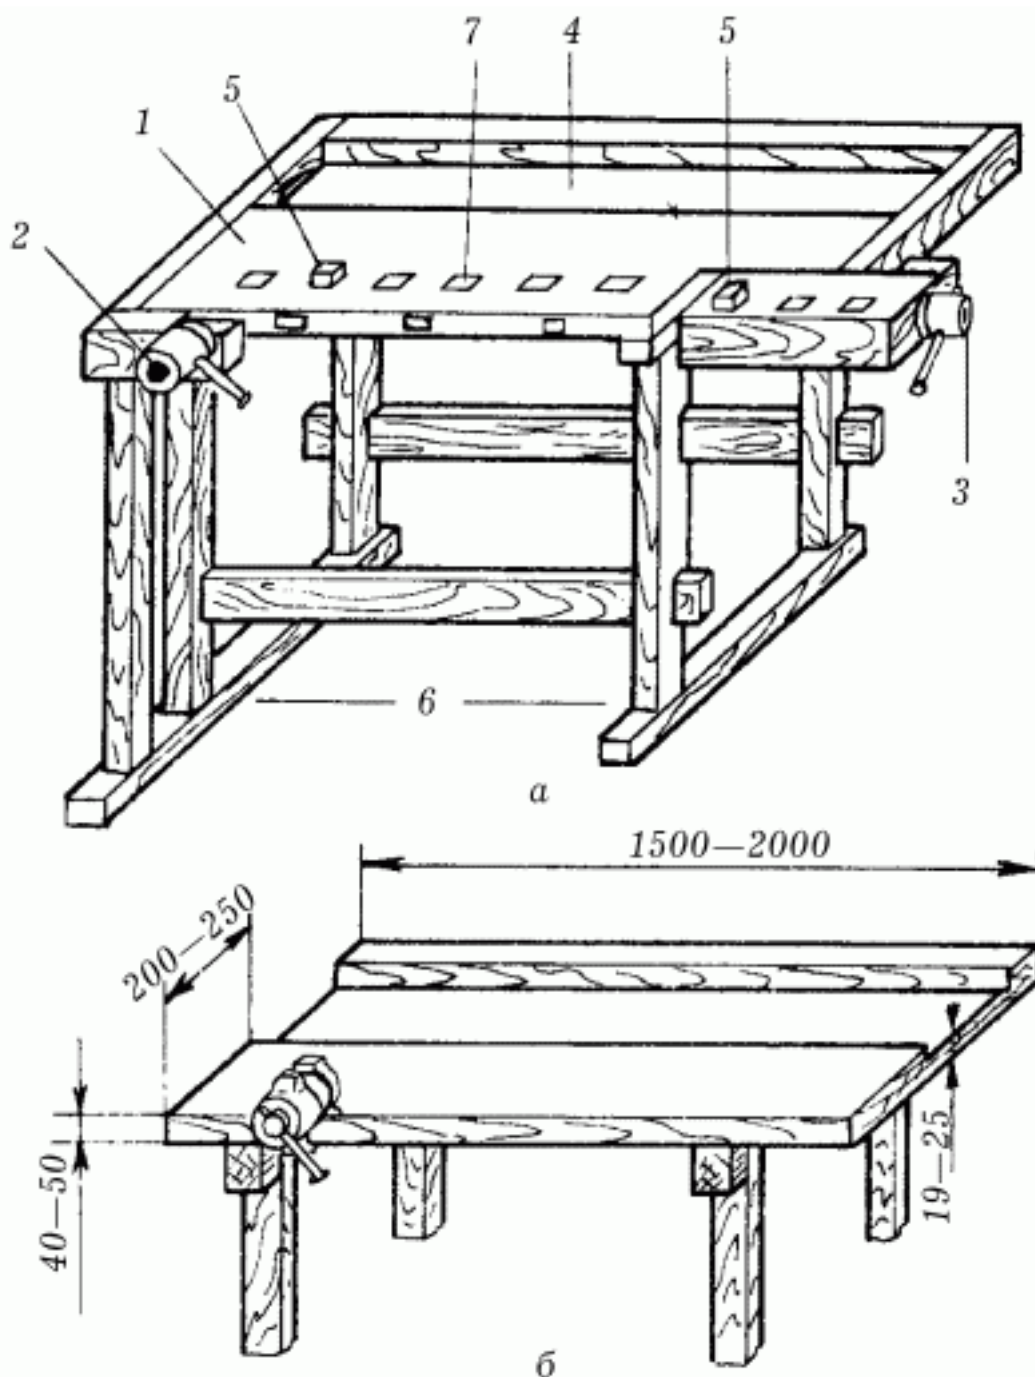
Столярный верстак (а) и верстачная доска со съемными тисками (б): 1 – верстачная доска; 2 – передние тиски; 3 – задние тиски с коробкой; 4 – лоток; 5 – клиновой упор; 6 – подверстачье; 7 – гнезда.
